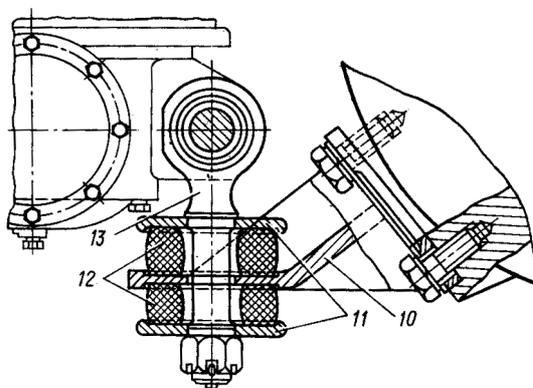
Конструкция опорно-осевого подвешивания тяговых двигателей через резиновые шайбы
